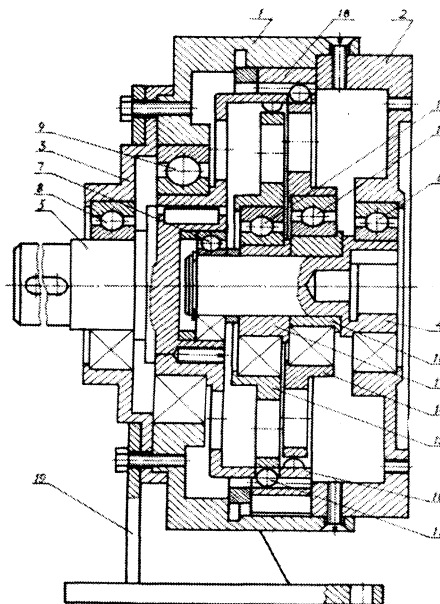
Конструктивная схема опытного образца шариковой радиально-плунжерной передачи
